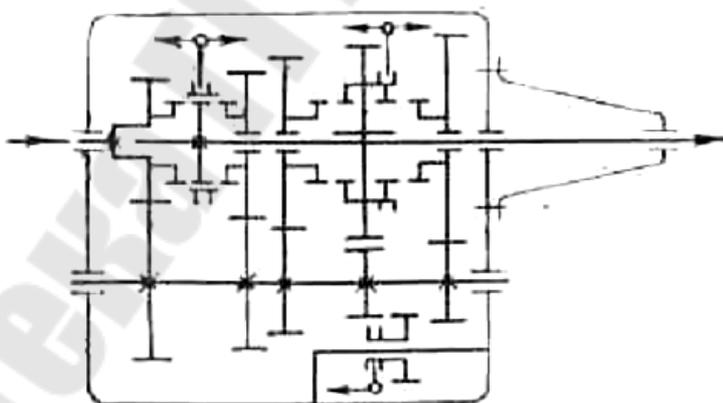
Кинематическая схема трехвальной четырехступенчатой коробки передач
